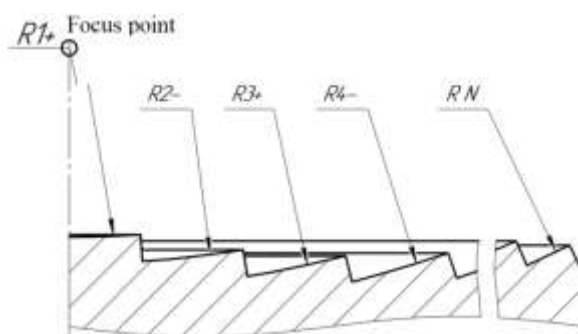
Схема Фокусирующего излучателя со ступенчато-радиальным профилем излучающей поверхности
